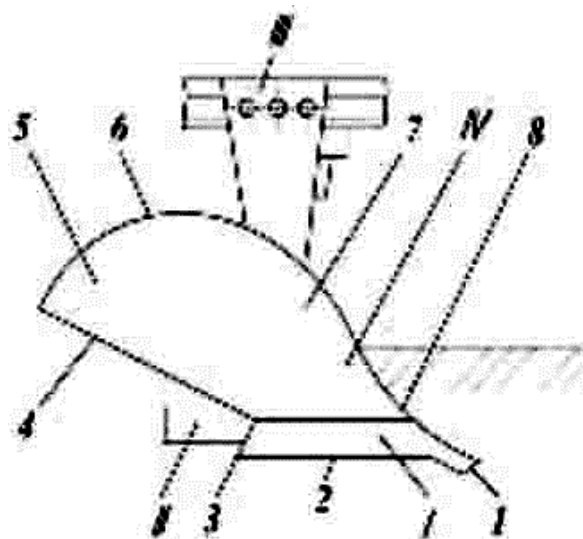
Лемешно-отвальный корпус плуга: *I* – лемех; *II* – полевая доска; *III* – стойка; *IV* – отвал; 1 – носок лемеха; 2 – лезвие; 3 – пятка; 4, 6, 8 – соответственно бороздной, верхний и полевой обрезы; 5 – крыло; 7 – грудь отвала
